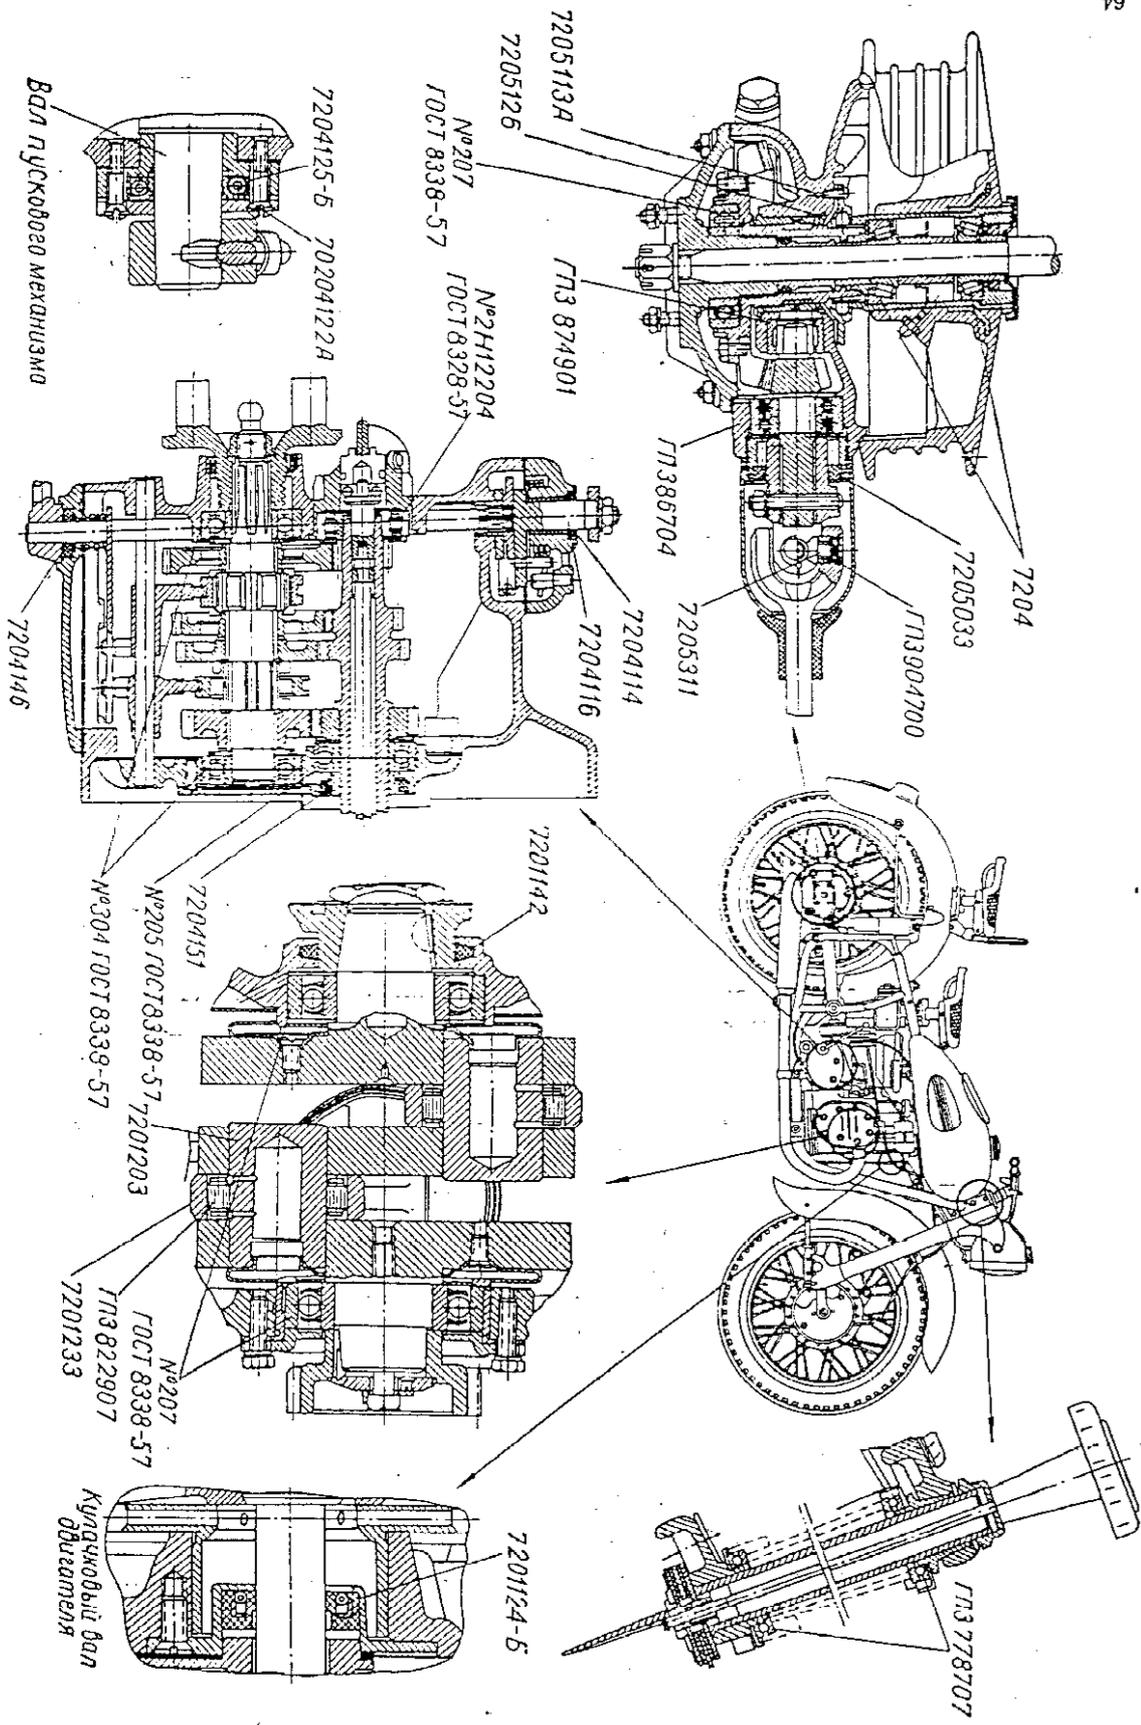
Схема расположения сальников и подшипников на мотоцикле.
